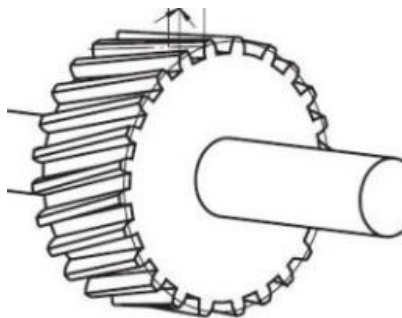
Vista isométrica de un engranaje helicoidal.
